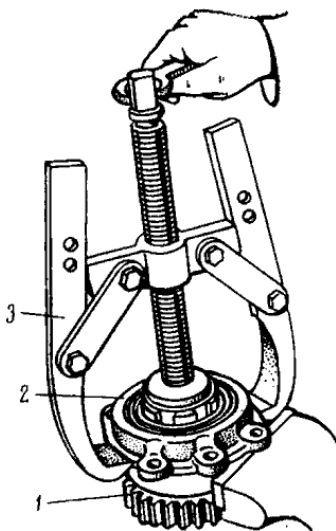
Выпрессовка ведущей шестерни II ступени редуктора из стакана: 1 — шестерня; 2 — стакан; 3 — съемник
